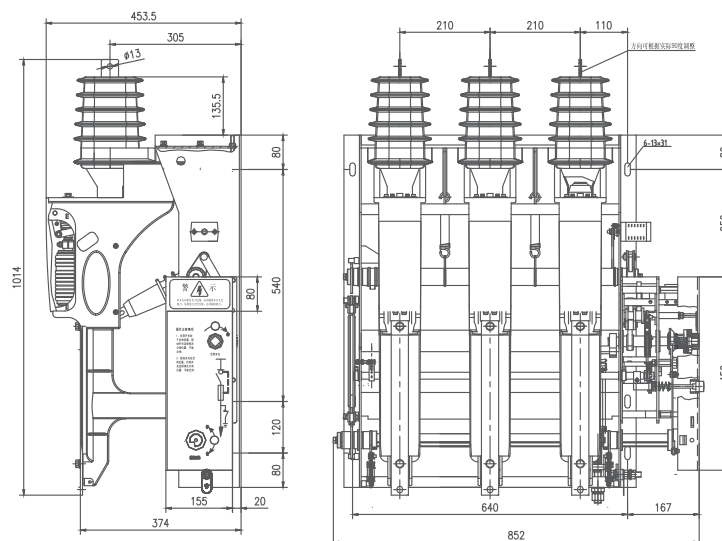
FZN25A-12D/630-20负荷开关外形尺寸及安装尺寸
